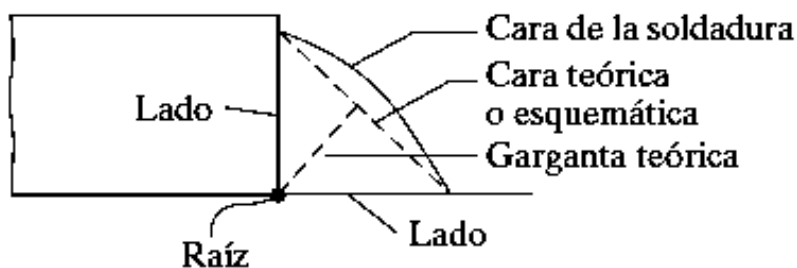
Soldadura Superficie Convexa de lados iguales
